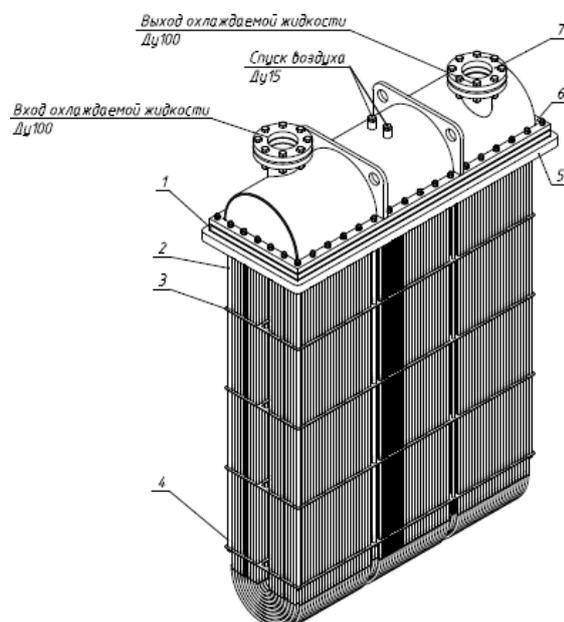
Чертеж общего вида судового охладителя погружного типа
